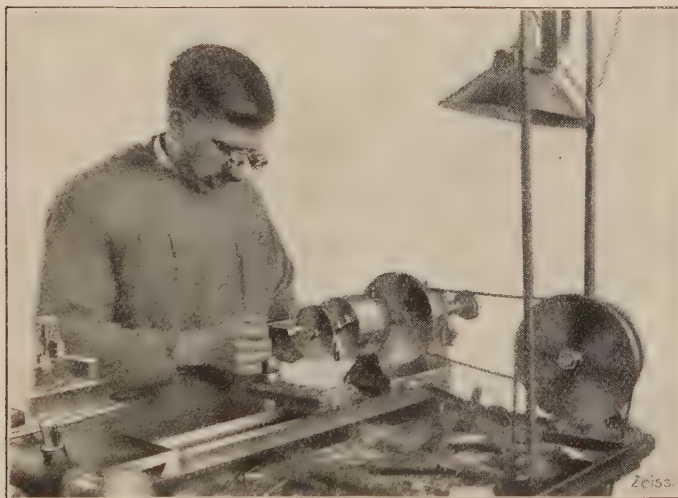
H. H. (Soldat) mit seiner Fernrohrbrille bei der Arbeit.
